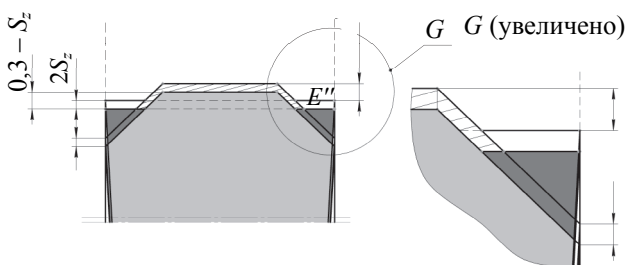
Схема формирования пропила дисковой твердосплавной пилой с плоско-трапецевидным профилем зубьев
